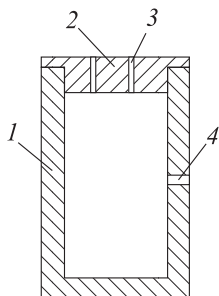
Схема тигля для выплавки меди: 1 – тигль; 2 – крышка; 3 – отверстие для выхода воздуха; 4 – отверстие для дутья
